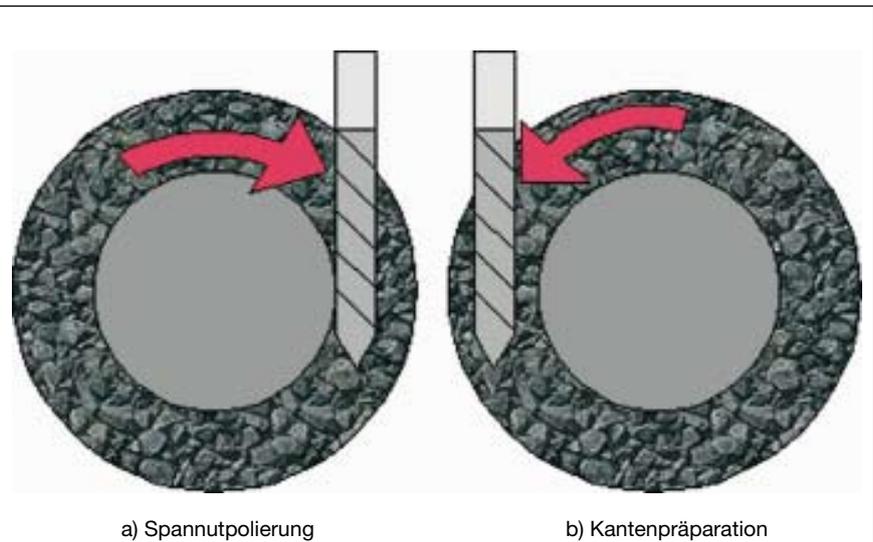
Gleichmäßiger Bearbeitungsdruck über die Länge des Werkzeuges
